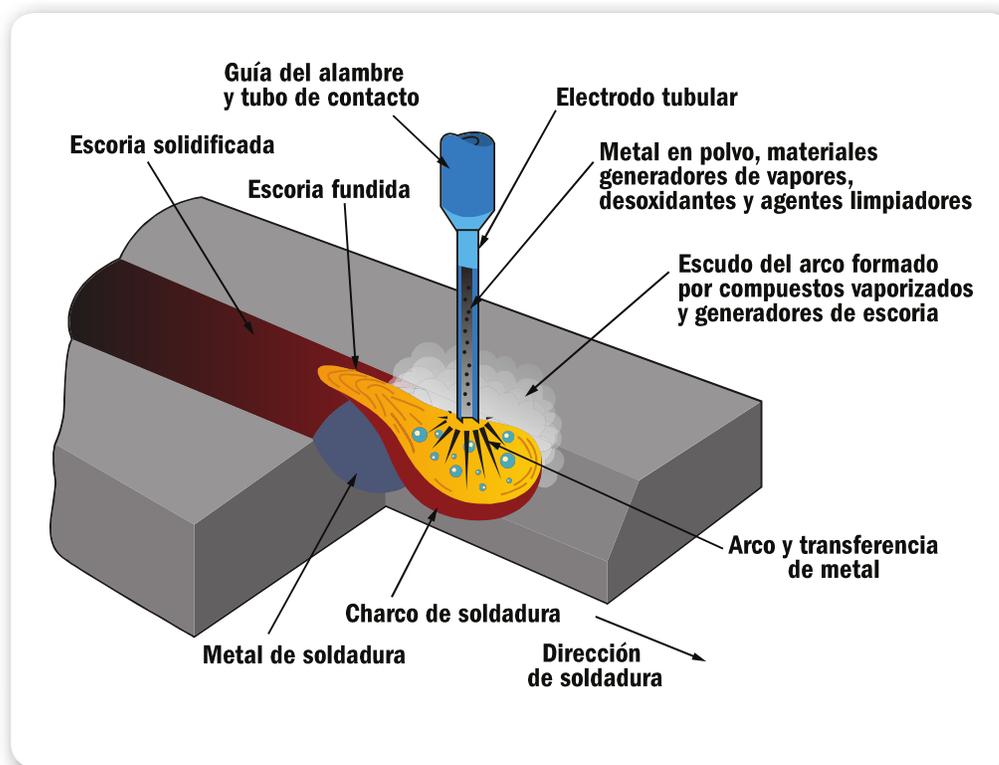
Partes que componen una soldadura por arco eléctrico y descripción de un electrodo tubular.
